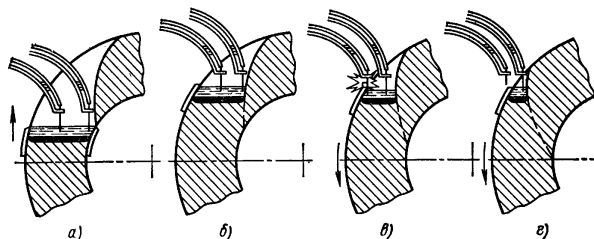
Схема сварки замыкающей части кольцевого шва
